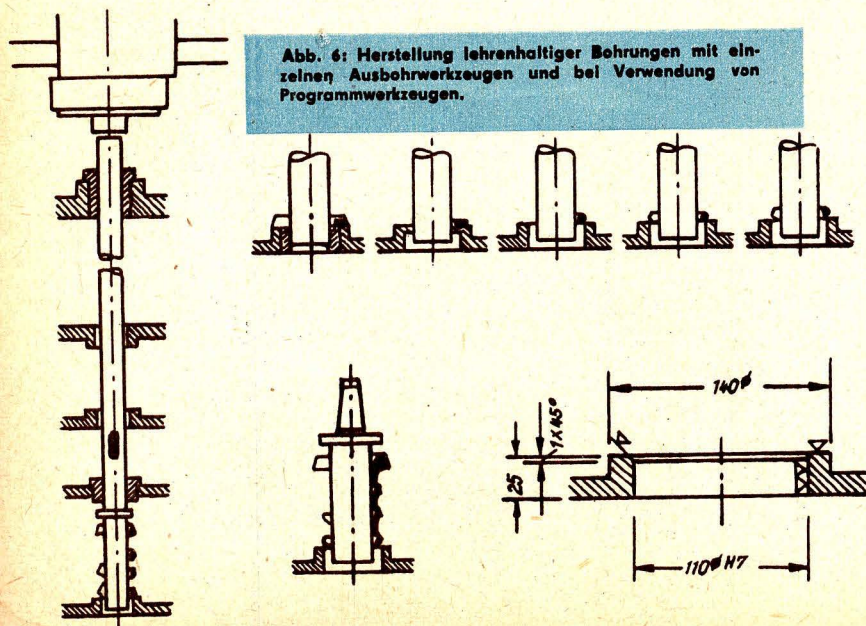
Herstellung lehrenhaltiger Bohrungen mit einzelnen Ausbohrwerkzeugen und bei Verwendung von Programmwerkzeugen.
